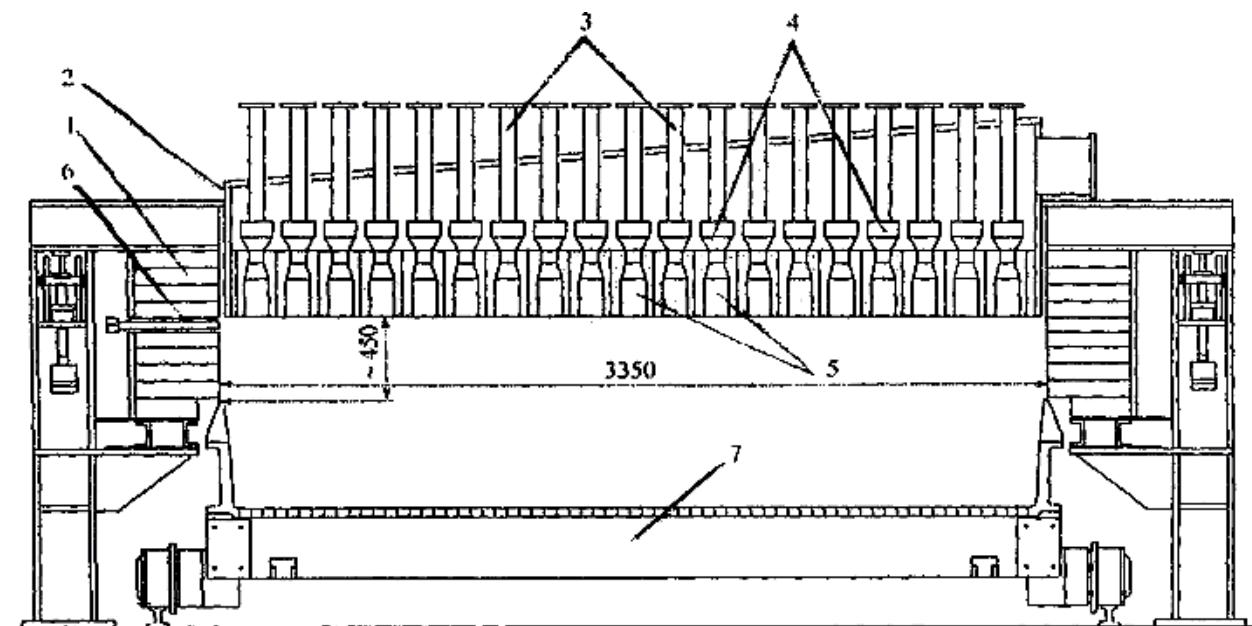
Поперечний розріз горна агломераційної машини АКМ - 75
